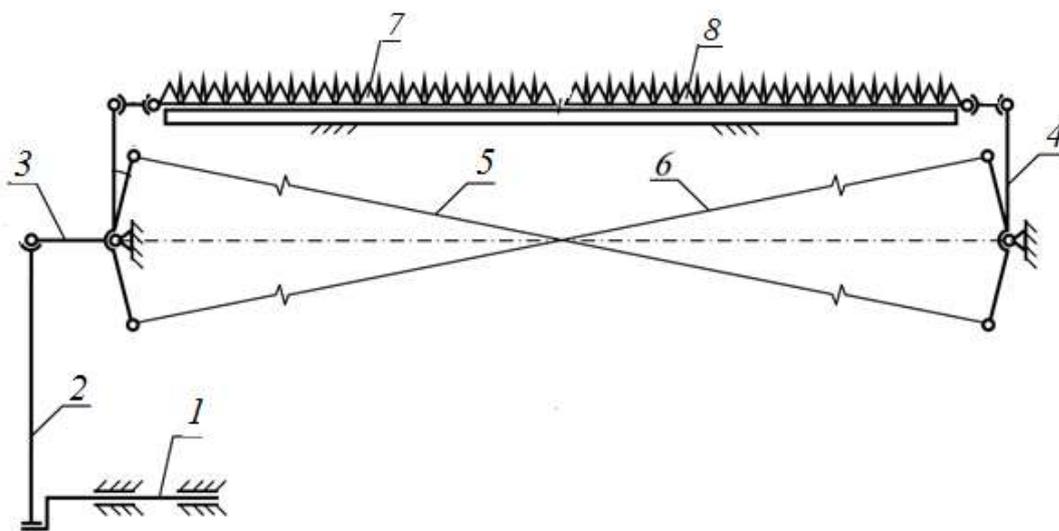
Схема кривошипно-коромыслового механизма двухножевого режущего аппарата с гибкими тягами
